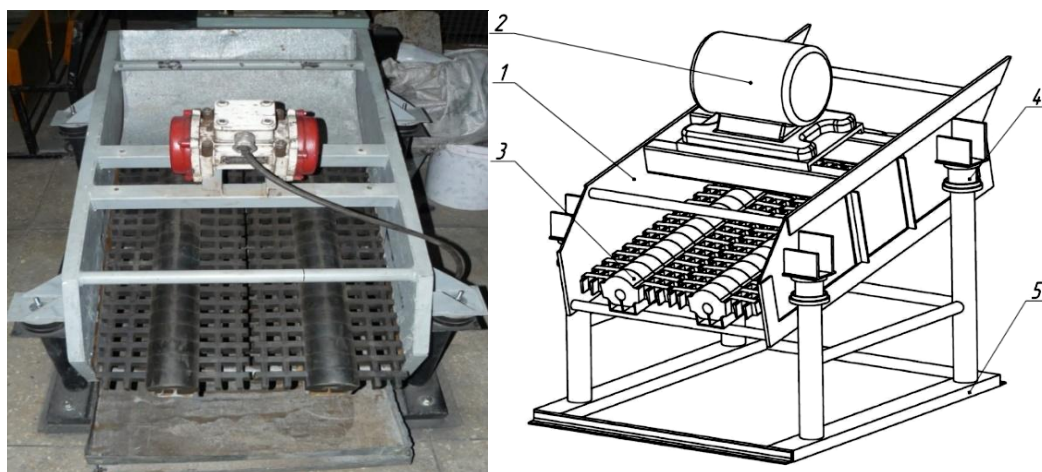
Загальний вид вібраційного грохота: 1 – короб;
